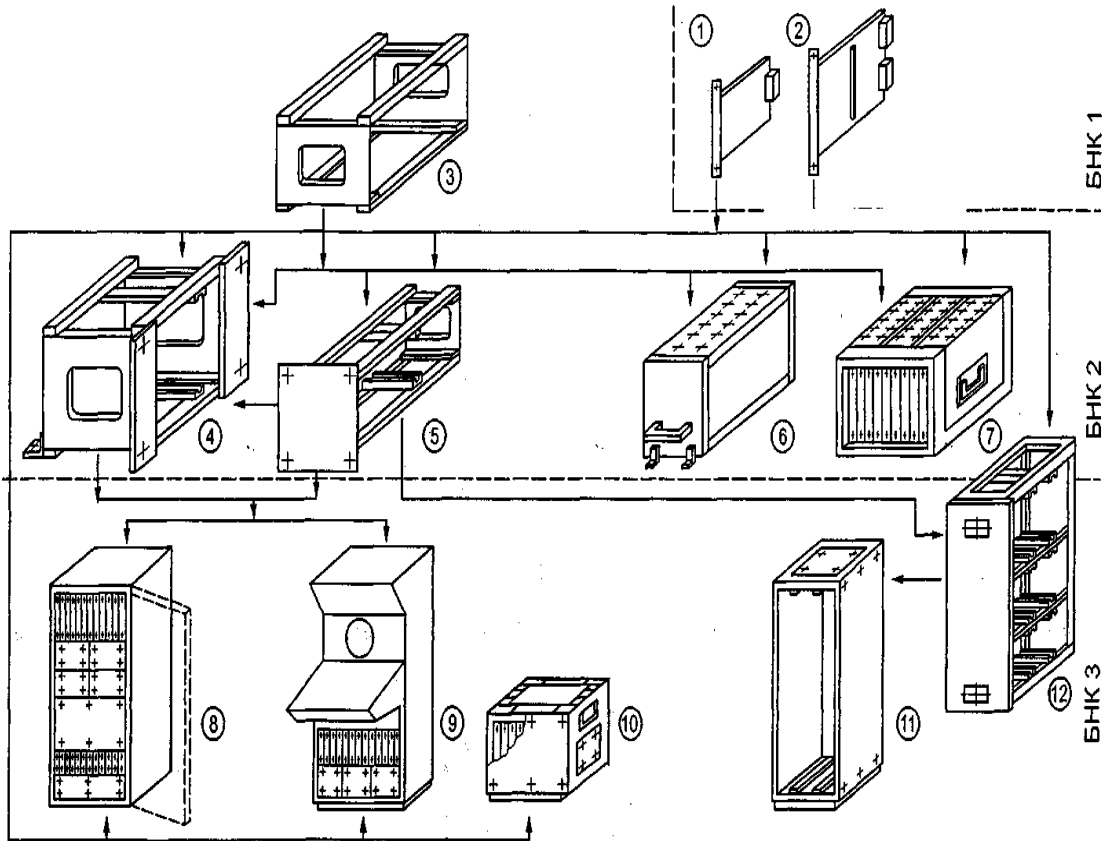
Система построения и входимости БНК РЭС [42]: 1, 2 - ячейки; 3 - корпус блока; 4 - блочный каркас; 5 - корпус вставного блока; 6 - корпус блока (авиационного); 7 - корпус контейнера (авиационного); 8 - корпус шкафа; 9 - корпус пульта; 10 - корпус моноблока; 11 - корпус шкафа для выдвигной стойки; 12 - выдвигная стойка
